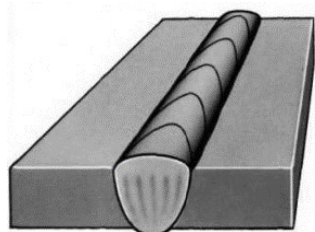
З'єднувальний шов, який виконаний лазерним зварюванням
